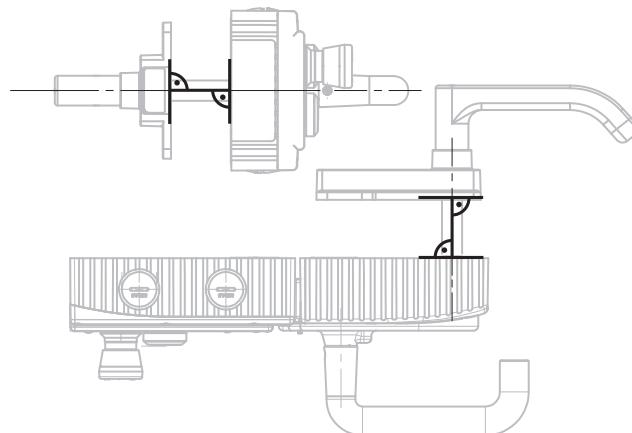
Monteringsexempel för högersvängd dörr (översiktsbild)
